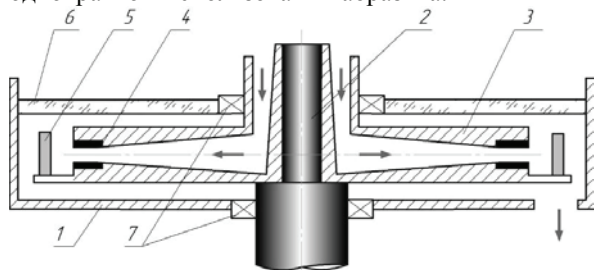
Схема испытательного узла стенда (1-камера, 2-вал, 3-ротор, 4-сопла, 5-образцы, 6-крышка, 7-уплотнения).
